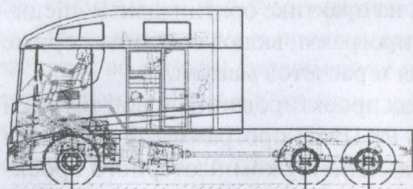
Компоновочный чертеж со схематически изображенными основными узлами и агрегатами
